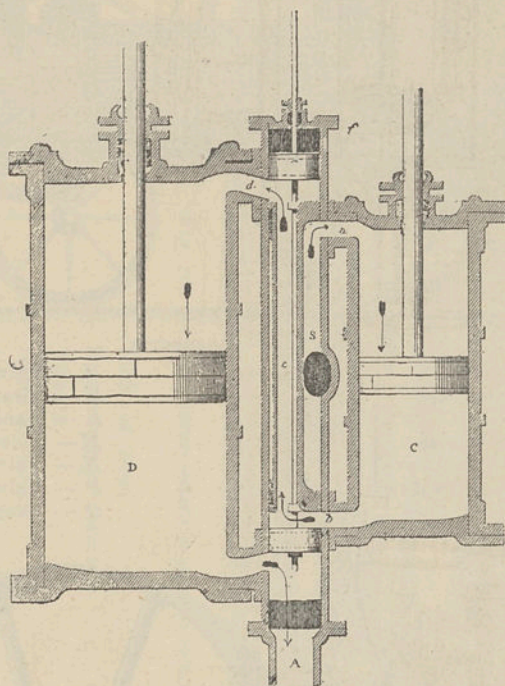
CYLINDROS DE UMA MACHINA WOOLF
